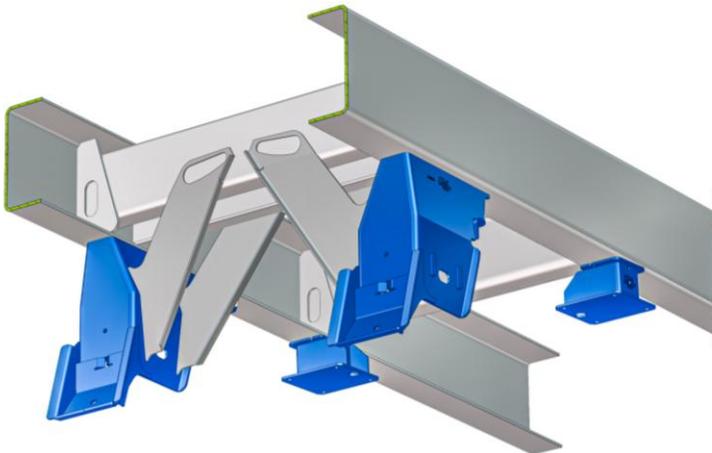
Reforço de ligação da travessa e suporte frontal – AirSuper HD
